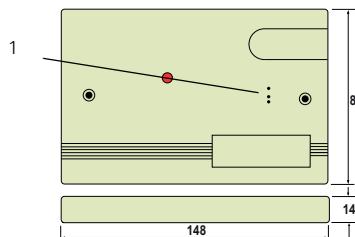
Placa de carcasa/ FC410SNM Frontansicht/
